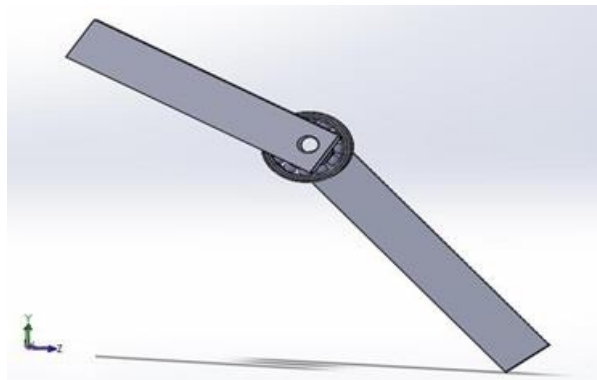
Diseño en solidworks del mecanismo del rodaje.
